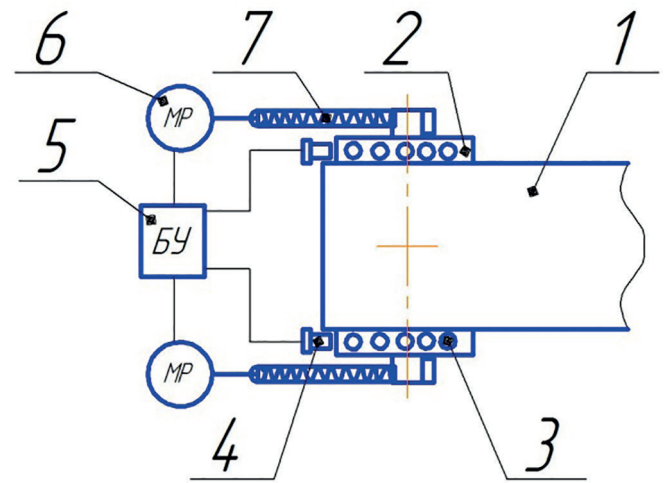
Схема установки для автоматичного натягу стрічки та центрування її положення в горизонтальній площині
